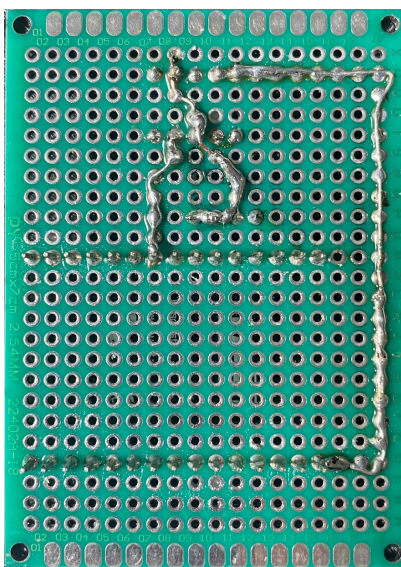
Processo de soldagem das *pistas* da PCB
